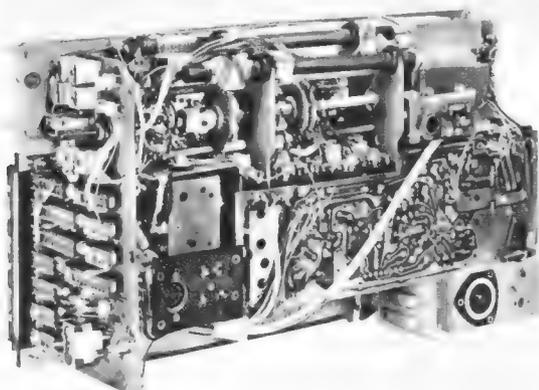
Chassis-Ansicht des Reiseempfängers Intercontinental
